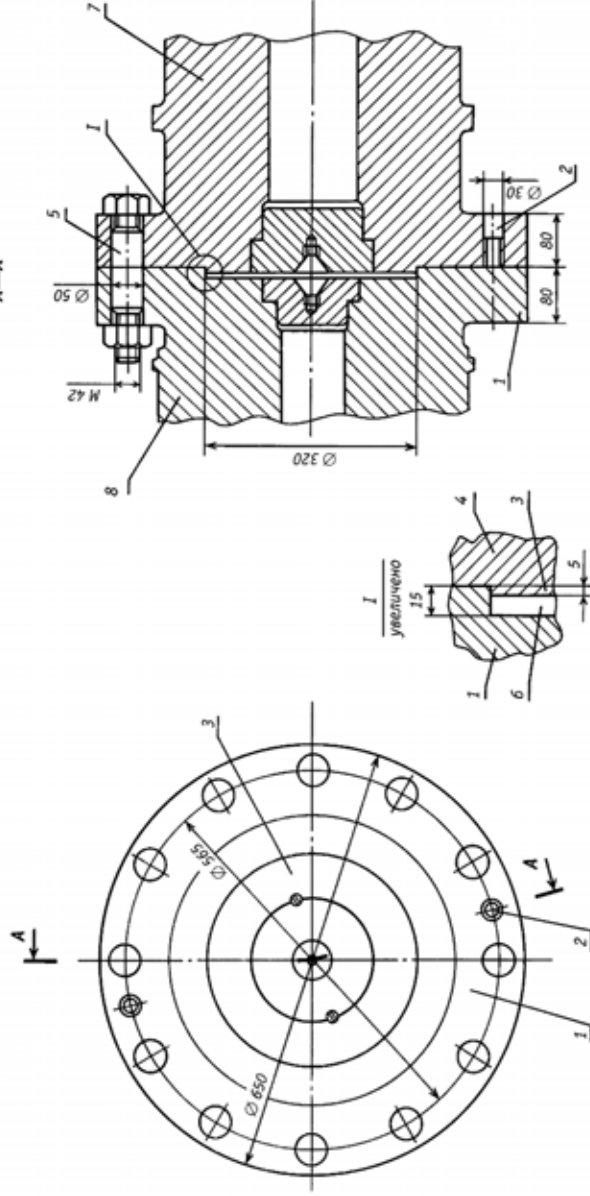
Жесткая муфта соединения ротора высокого и среднего давления турбины К-300-240: 1 – фланец полумуфты ротора ЦВД; 2 – отверстие с резьбой для отжимного болта; 3 – кольцевой выступ; 4 – фланец полумуфты ротора ЦСД; 5 – призонный болт; 6 – впадина; 7 – ротор ЦСД; 8 – ротор ЦВД
